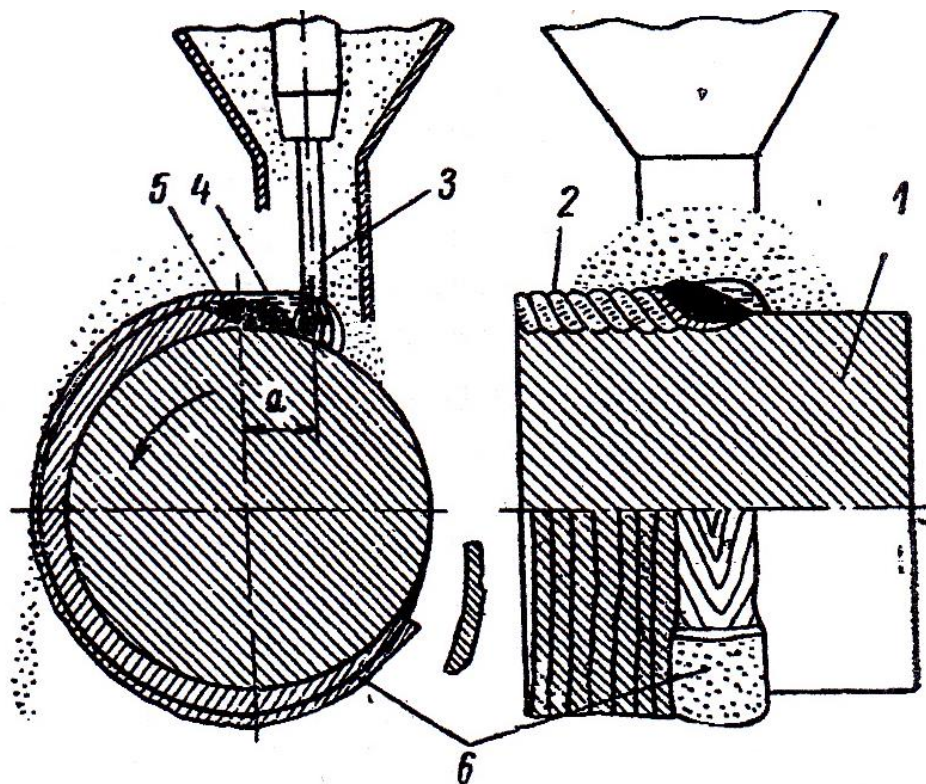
Схема наплавлення тіла обертання під флюсом:
